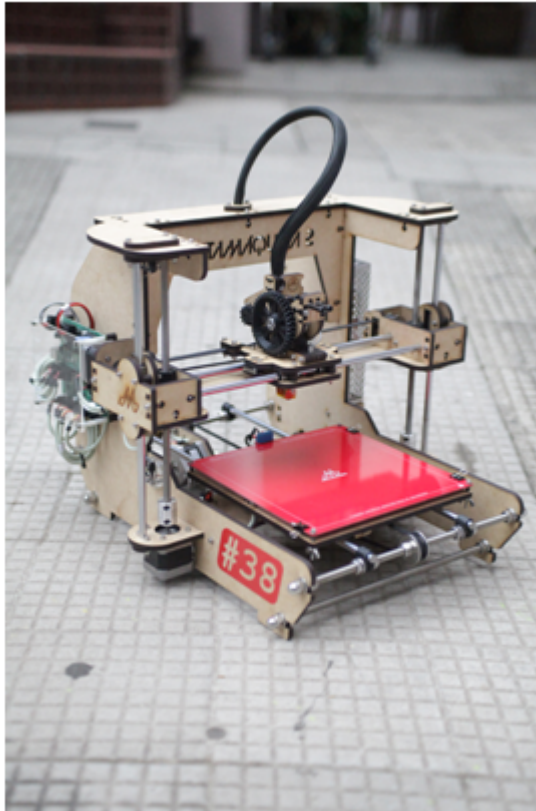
Disponível em: [<http://metamaquina.com.br>]
